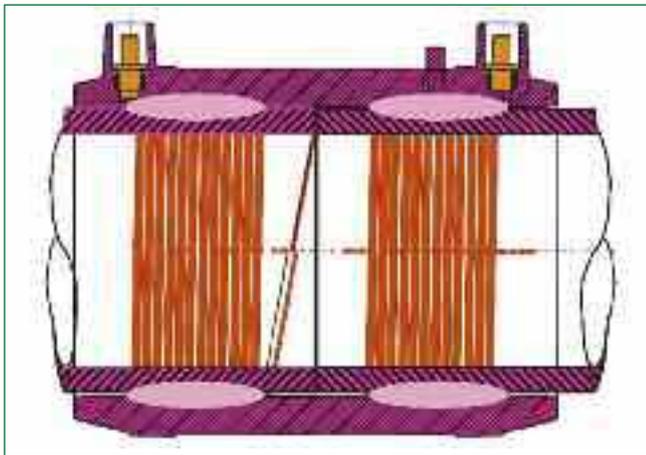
Prinzip der Heizwendelschweißtechnik
